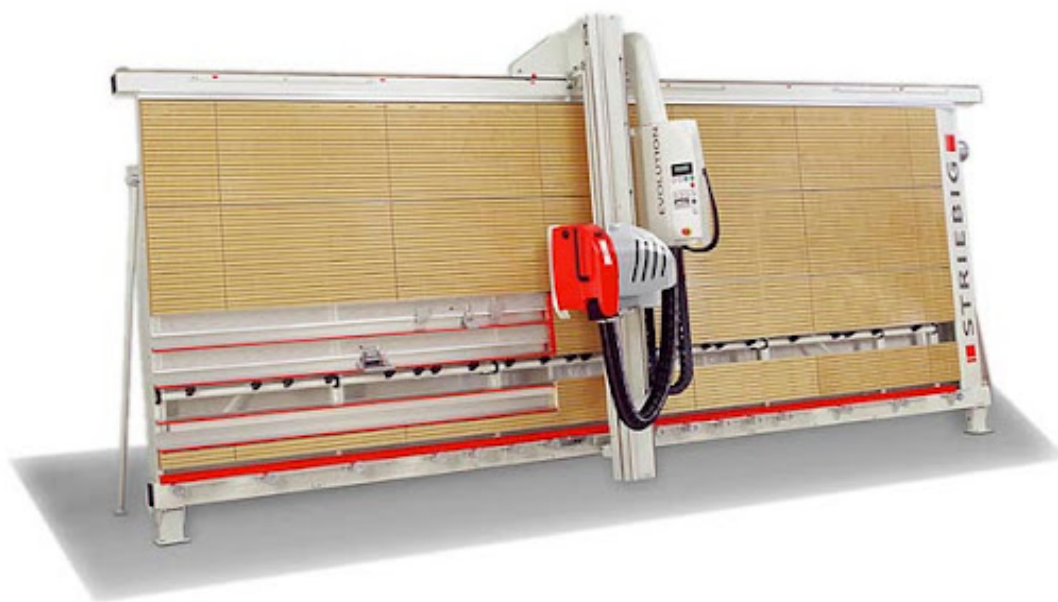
Вертикальний форматно-розкроювальний верстат.
